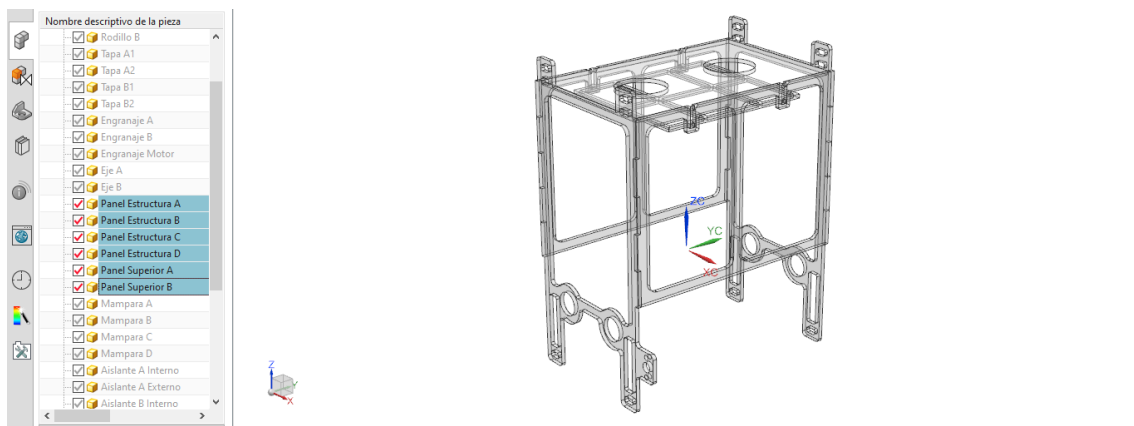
Componentes en metacrilato fabricados por corte láser / Fuente: Propia
